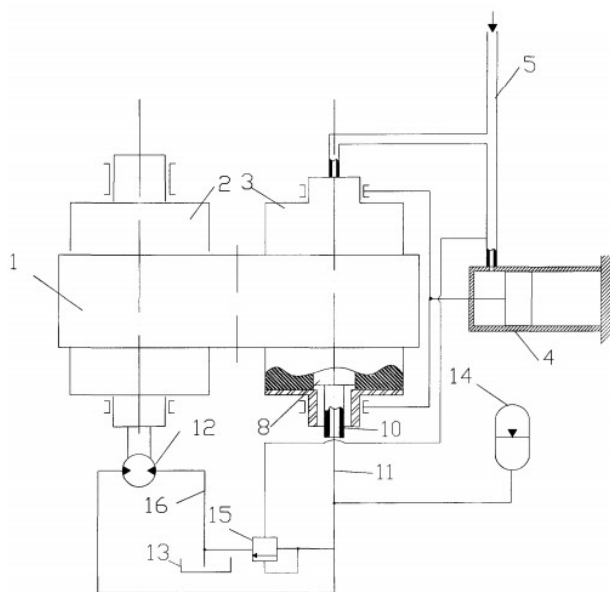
Загальний вигляд стрічкового конвеєру: 1 — стрічка, 2 — приводний барабан, 3 — натяжний барабан, 4 — механізм натягу, 5 — напірна магістраль, 6, 9 — пази, 7, 10 — канали, 8 — циліндр, 11 — напірна лінія, 12 — гідравлічний мотор, 13 — гідравлічний бак, 14 — акумулятор, 15 — захисний клапан, 16 — зливна магістраль
